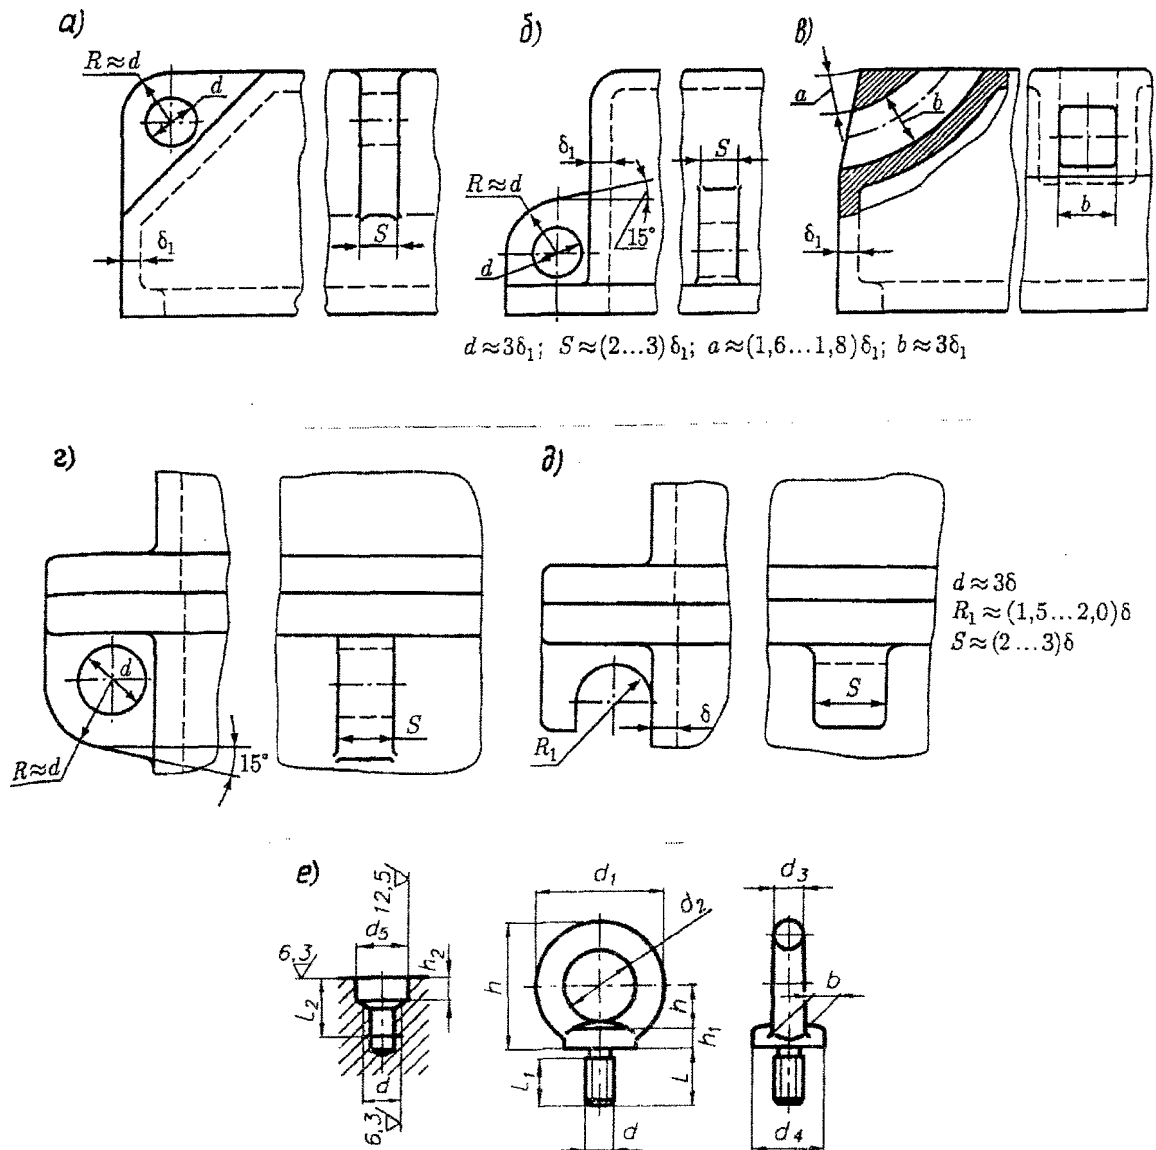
Устройства для подъема и транспортирования корпусных деталей и редуктора в сборе:
